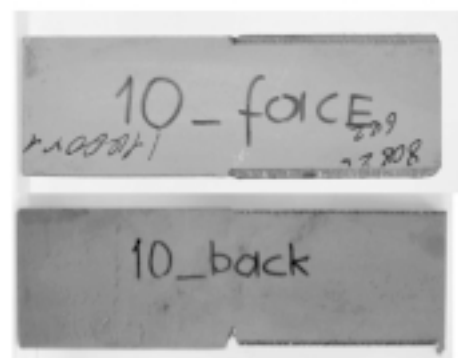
Вид тестовых заготовок для исследования причин погрешностей размеров деталей
